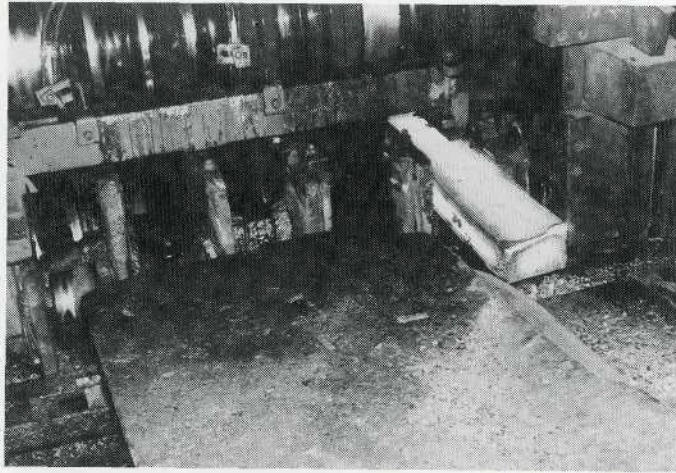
Detail van de railwalserij tijdens het gelijktijdig walsen van twee spoorstaven.
